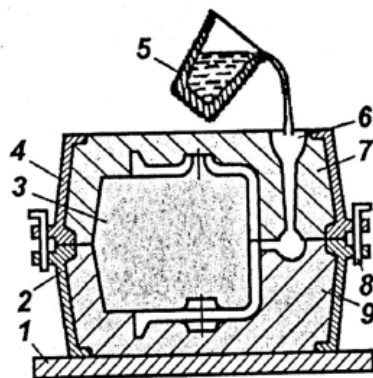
Заливка металла в опочную форму: 1 – подопочная плита; 2 – нижняя опока; 3 – стержень; 4 – верхняя опока; 5 – заливочный ковш; 6 – литниковая система; 7 – верхняя полуформа; 8 – скобы для крепления опок; 9 – нижняя полуформа
